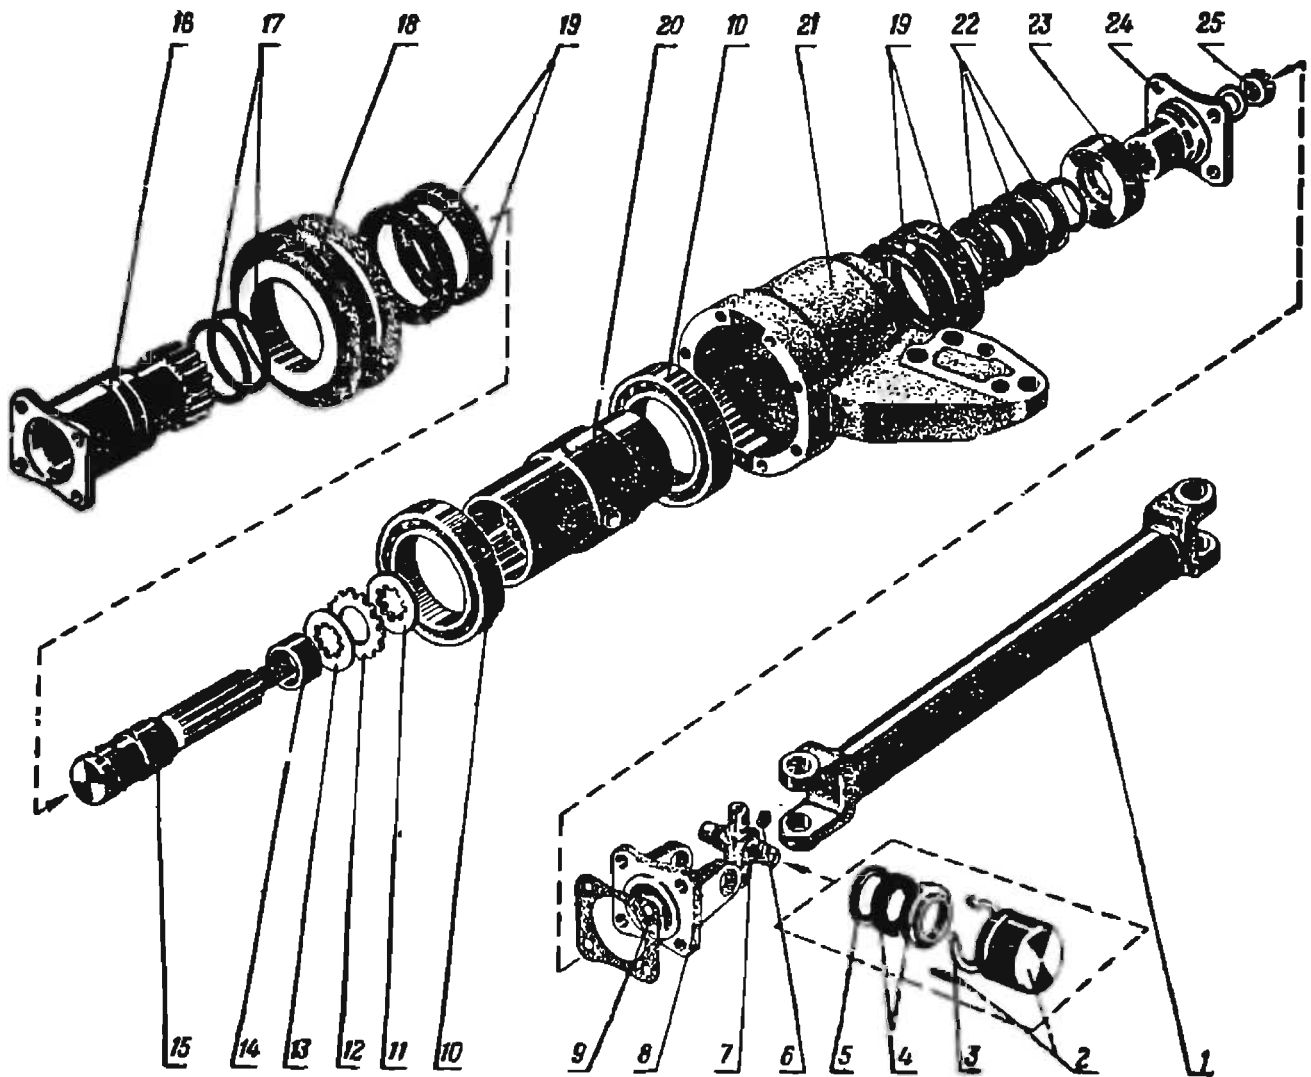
Карданный привод переднего ведущего моста с промежуточной опорой: 1 — карданный вал; 2 — игольчатый подшипник; 3 — стопорное кольцо; 4 — сальник крестовины в сборе; 5 — отражатель сальника карданного вала; 6 — пресс-масленка; 7 — крестовина; 8 — фланец кардана; 9 — прокладка; 10 — подшипники; 11 — нажимной диск; 12 — ведомый диск (13 шт.); 13 — ведущий диск (16 шт.); 14 — распорная втулка; 15 — вал промежуточной опоры; 16 — фланец скользящий; 17 — уплотнительные кольца; 18 — корпус манжеты; 19 — манжеты; 20 — втулка муфты; 21 — корпус промежуточной опоры; 22 — тарельчатые пружины; 23 — опорная шайба; 24 — фланец карданного вала; 25 — гайка.
